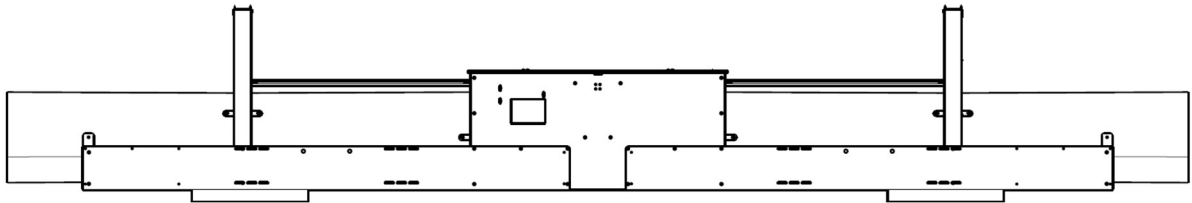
Falle mit Grundrahmen auf Betonplatten
